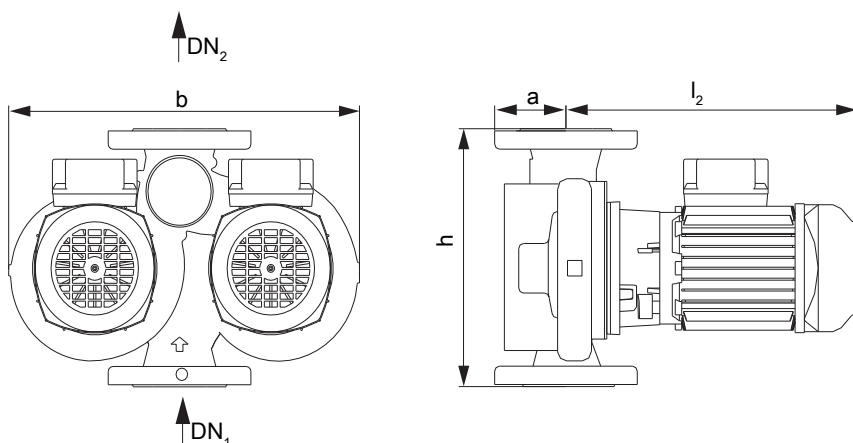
Размеры насосного агрегата с фланцевым соединением, типоразмер \geq 032-032-100
